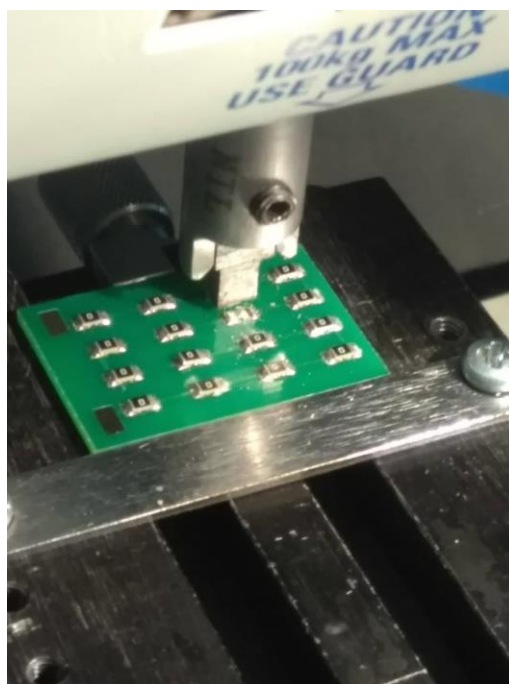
Přístroj PC 2400 od firmy Dage pro zkoušku stříhem
